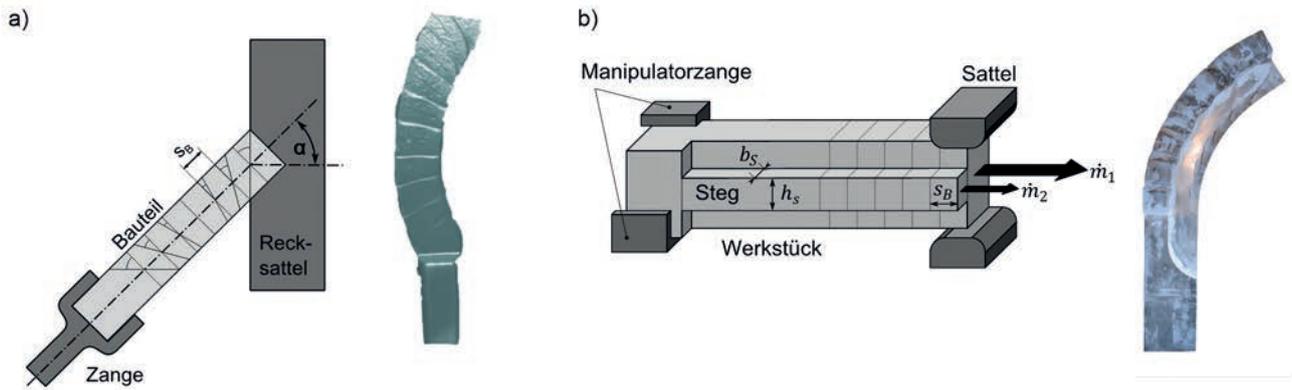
a) Schrägecken [3], Draufsicht und Bauteilgeometrie. b) Schmieden eines profilierten Blocks [4], Draufsicht und Bauteilgeometrie.
